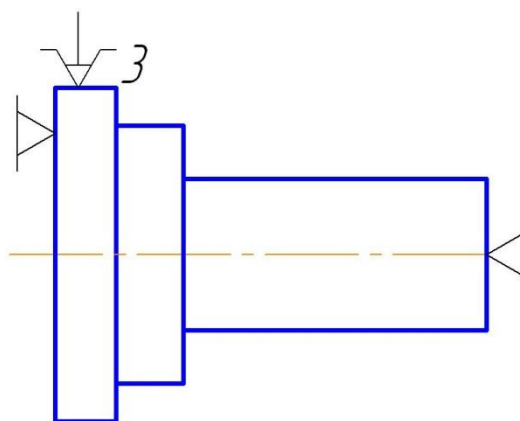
Умовна схема базування на свердлувальному верстаті з ЧПК
